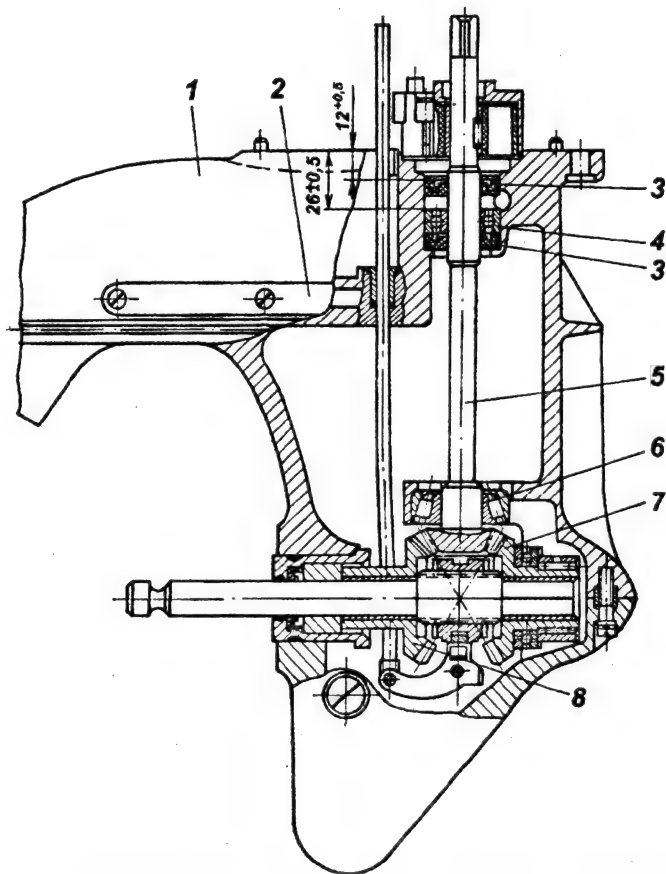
Редуктор моторов семейства «Вихрь» новой конструкции
